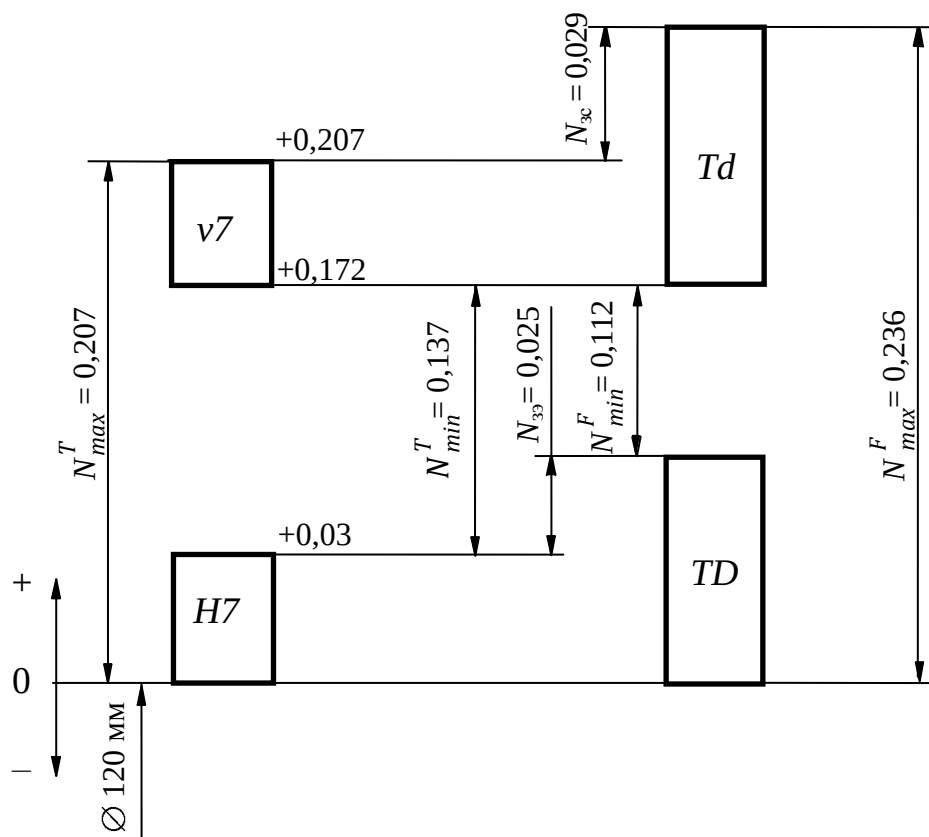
Схема полей допусков посадок с натягом
